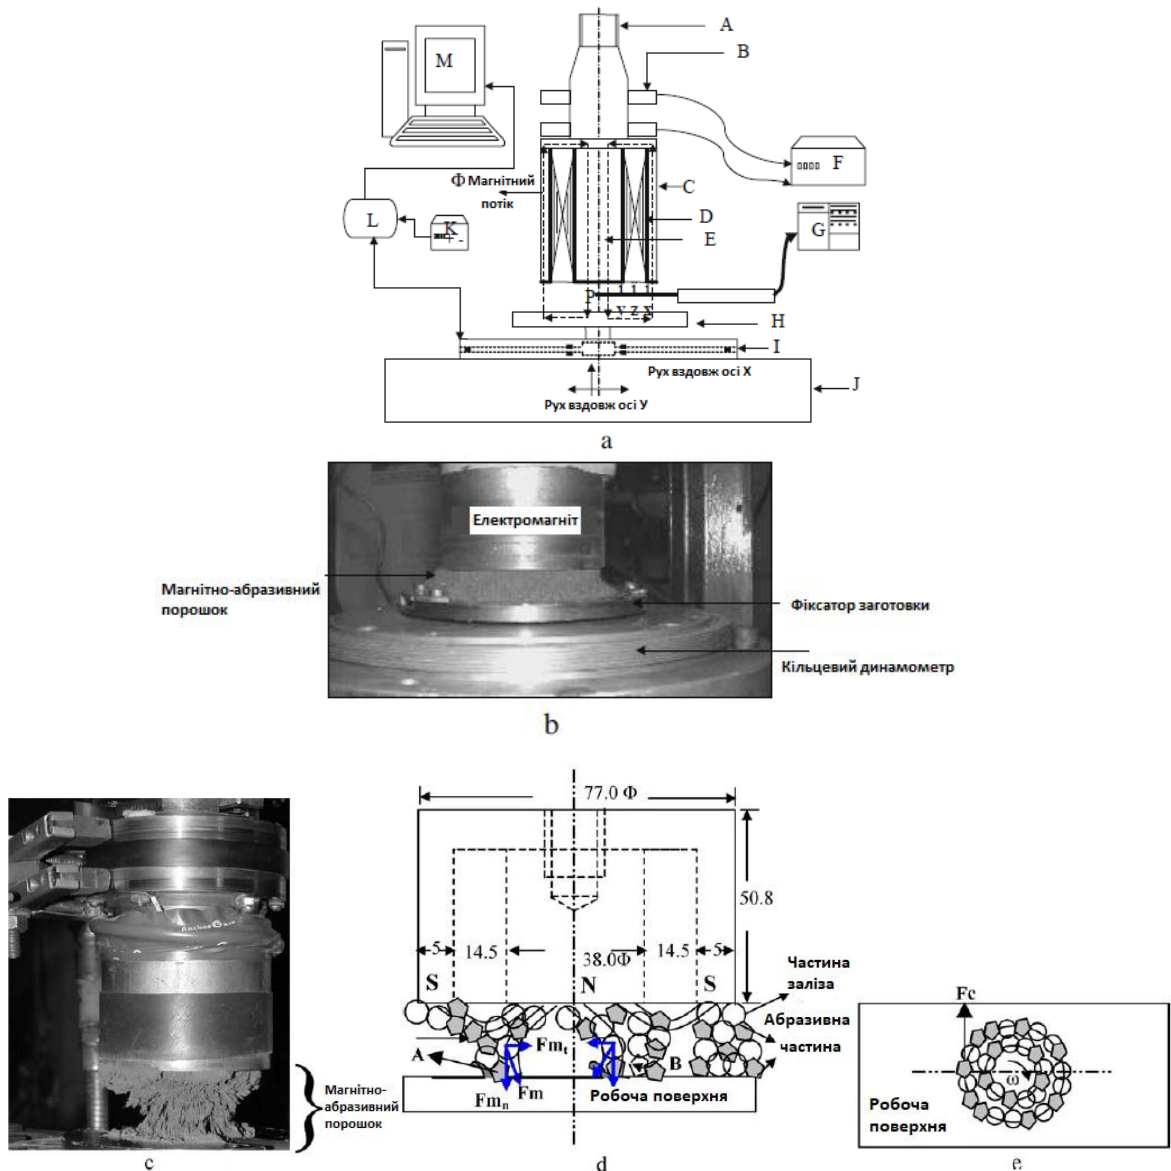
(а) –Схема установки магнітно-абразивної обробки площини. А – Головний шпиндель вертикального фрезерного верстата, кільця В ковзання, зовнішній полюс С (південний полюс), котушка D, центральний полюс Е (північний полюс), джерело живлення постійного струму F, цифровий вимірювач Гаусса G, динамометр I, J – стіл верстата, К - 6,0 В пост. струму для блоку формування сигналу, блок формування сигналу L, М – ПК для запису даних сили, Р – вимірювач Гаусса; (б) – Фотографія гнучкої магнітної абразивної щітки; (с) - Фотографія ГМАЩ при великому робочому зазорі при заповненні магнітними абразивними частинками. (д) – процес оброблення абразивними частинками і сили, що діють під час процесу MAO; (е) – обертання частинок на поверхні
